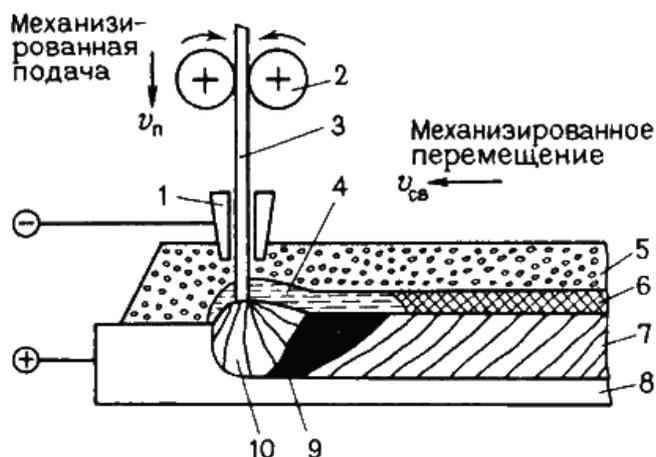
Схема автоматической дуговой сварки под флюсом
